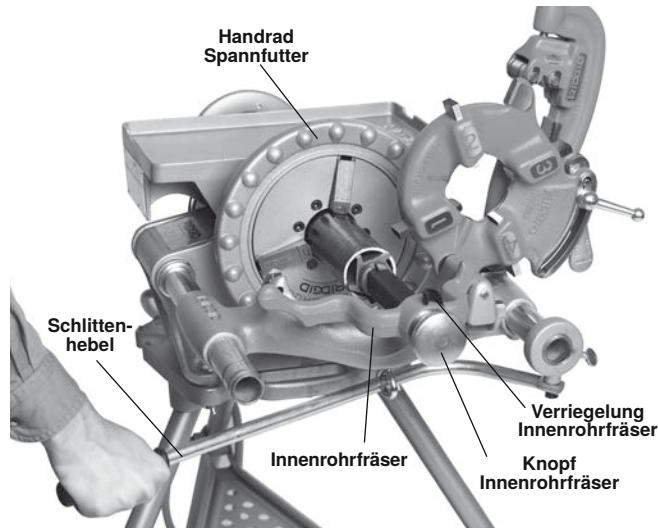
Entgraten mit 341 Innenrohrfräser
